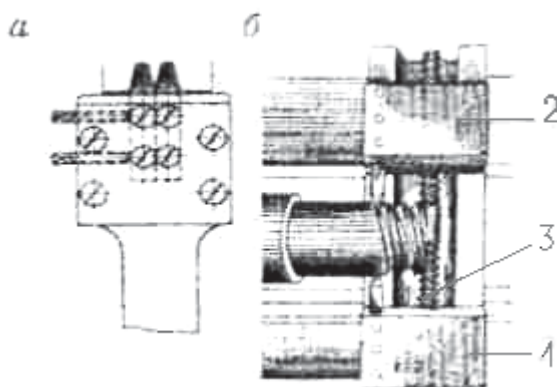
Резцедержатели для нарезания двухзаходных резьб: *а* – резцедержатель для двух резьб; *б* – специальное приспособление с двумя резцедержателями
